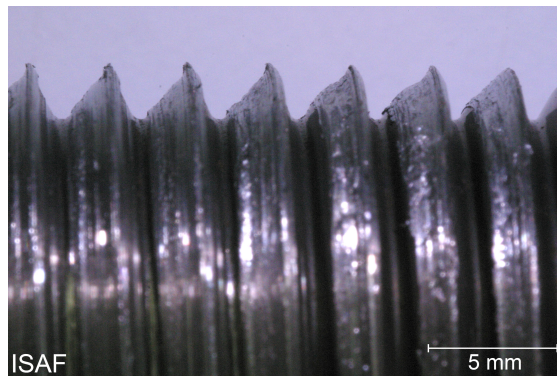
Gewindeprüfkörper axial belastet mit 200kN (Bolzen)
